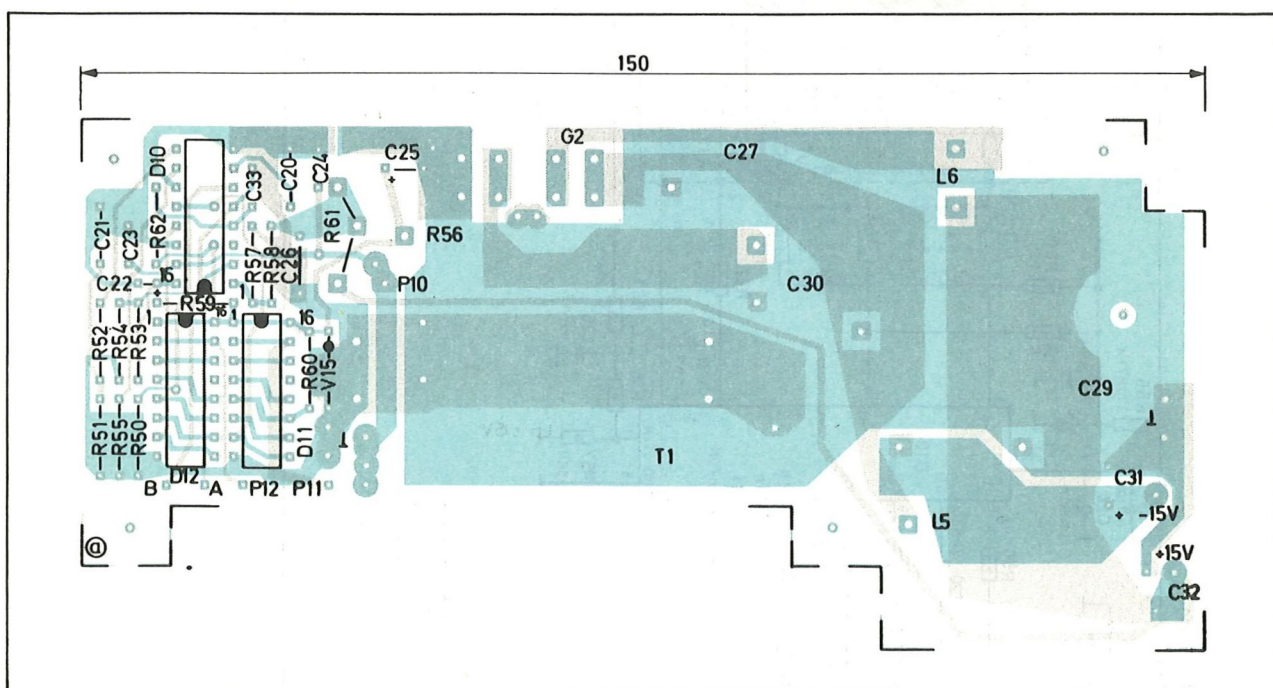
/13.4-6: Onderdelen plattegrond 15-V-print
